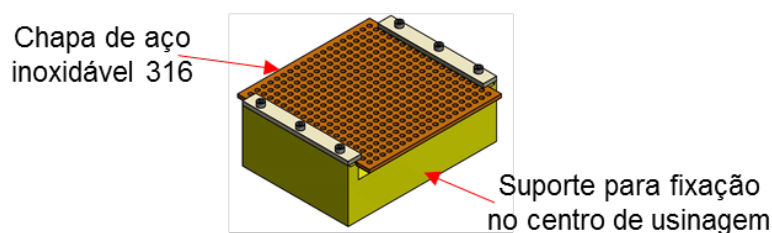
Chapa com suporte para fixação no centro de usinagem (Fonte: Autoria própria)
